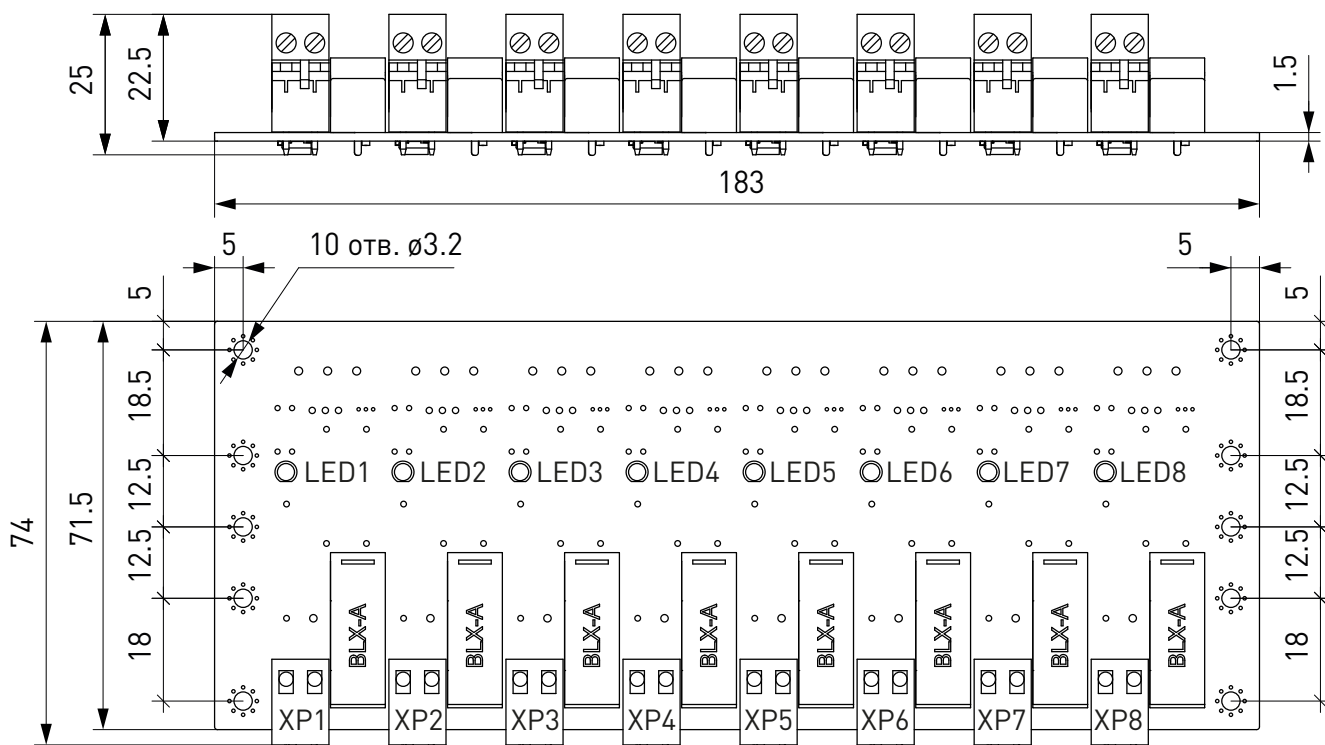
Габаритные размеры блока предохранителей PLP-8F-DC.
